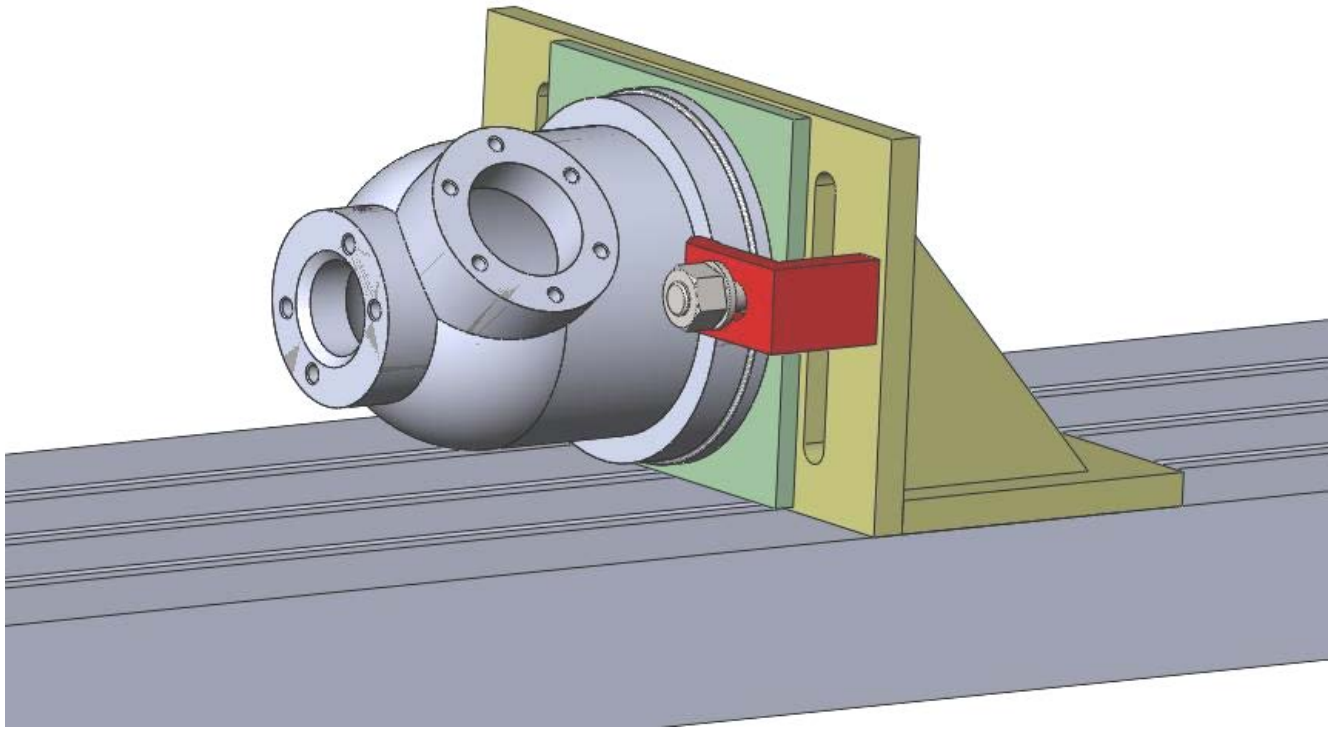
Теоретична схема базування для обробки комплекту поверхонь 6
